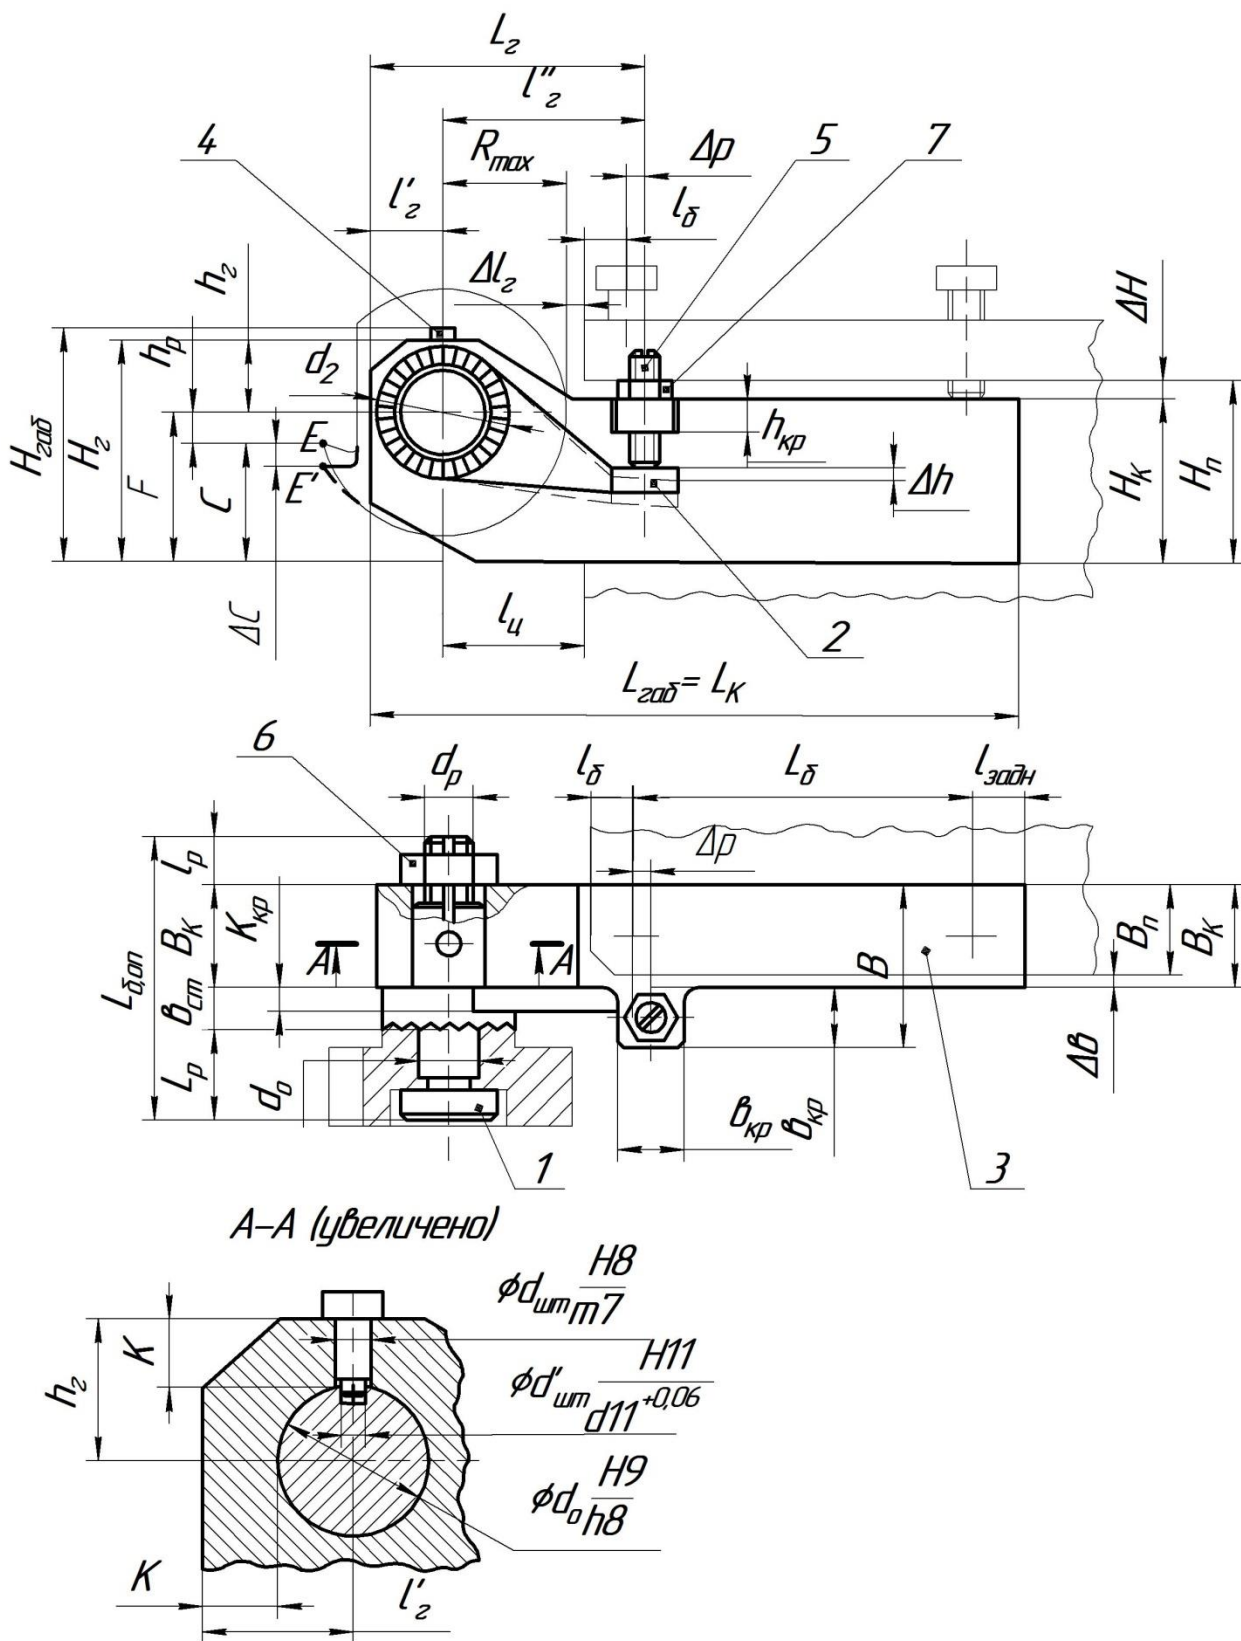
Державка для круглых фасонных резцов I типа:
